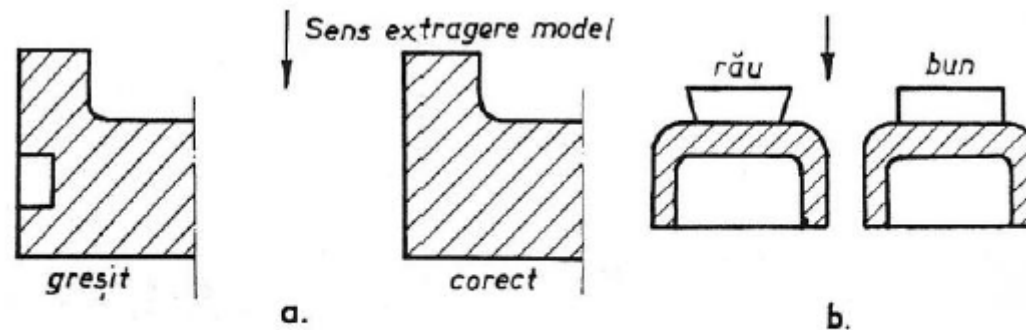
Exemple de formă geometrică piesă turnată în vederea extragerii ușoare a modelului.
